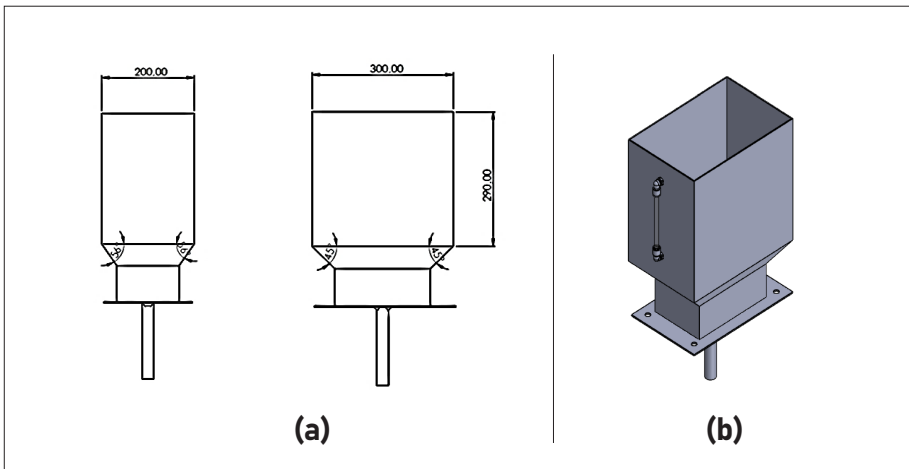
(a) Dimensiones de la tolva; (b) Diseño final tolva de agua.
